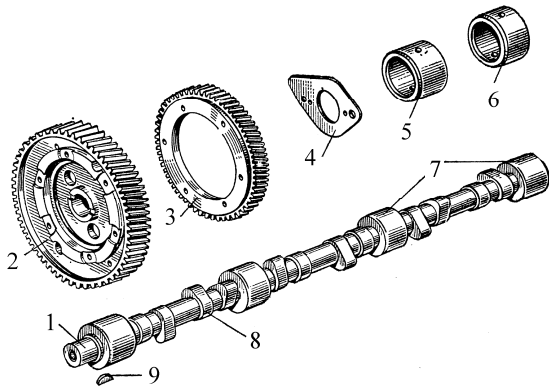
Распределительный вал и детали его привода: 1 – распределительный вал; 2 – шестерня привода вала; 3 – шестерня привода топливного насоса; 4 – упорный фланец; 5 – передняя опорная втулка; 6 – опорная втулка; 7 – опорные шейки; 8 – кулачки; 9 – шпонка
